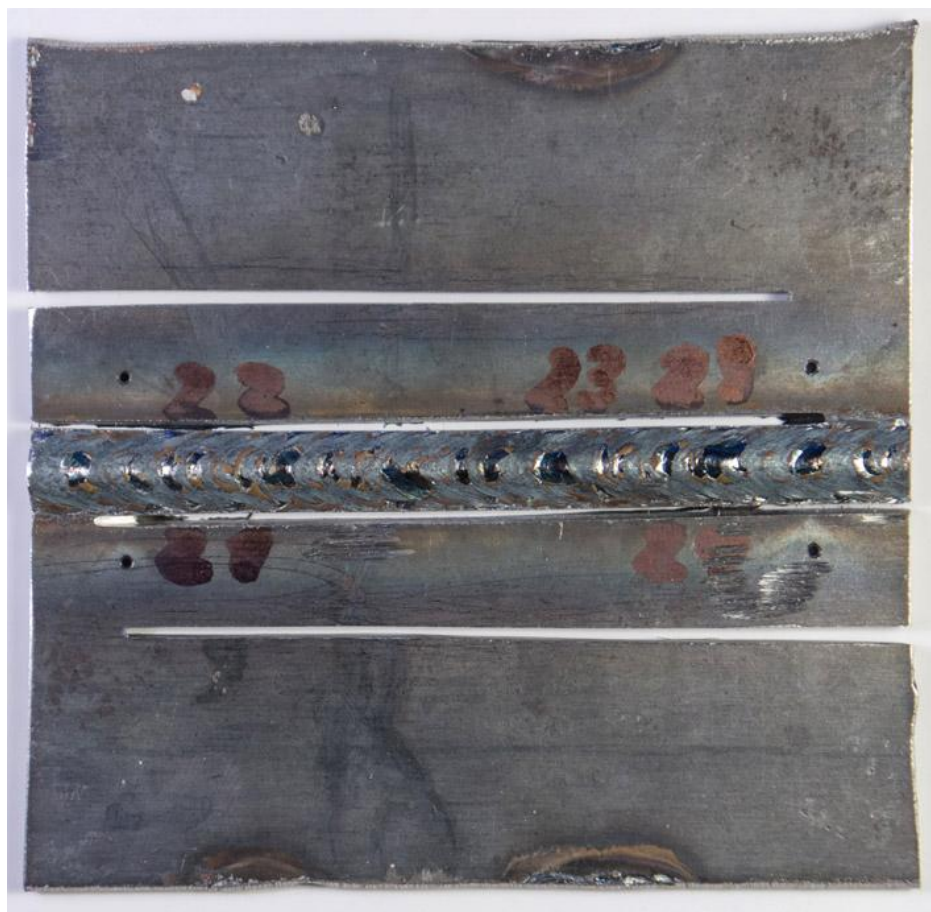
Вигляд зварного шва після вивільнення баз шляхом вирізання.
